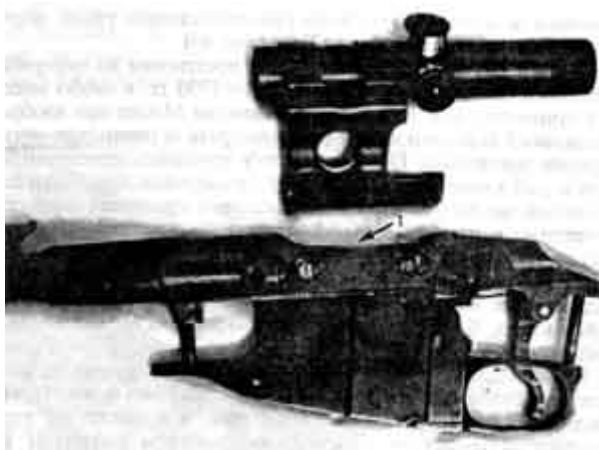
Основание кронштейна прицела ПУ для крепления на круглой ствольной коробке 1
